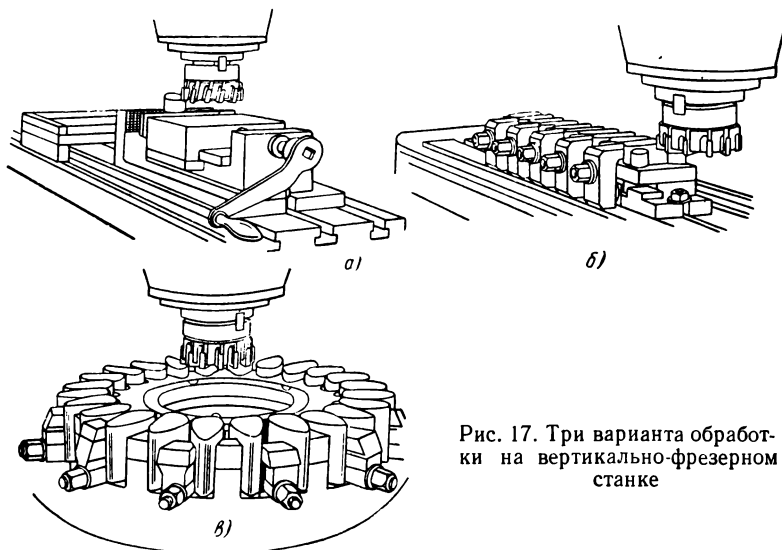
Три варианта обработки на вертикально-фрезерном станке
